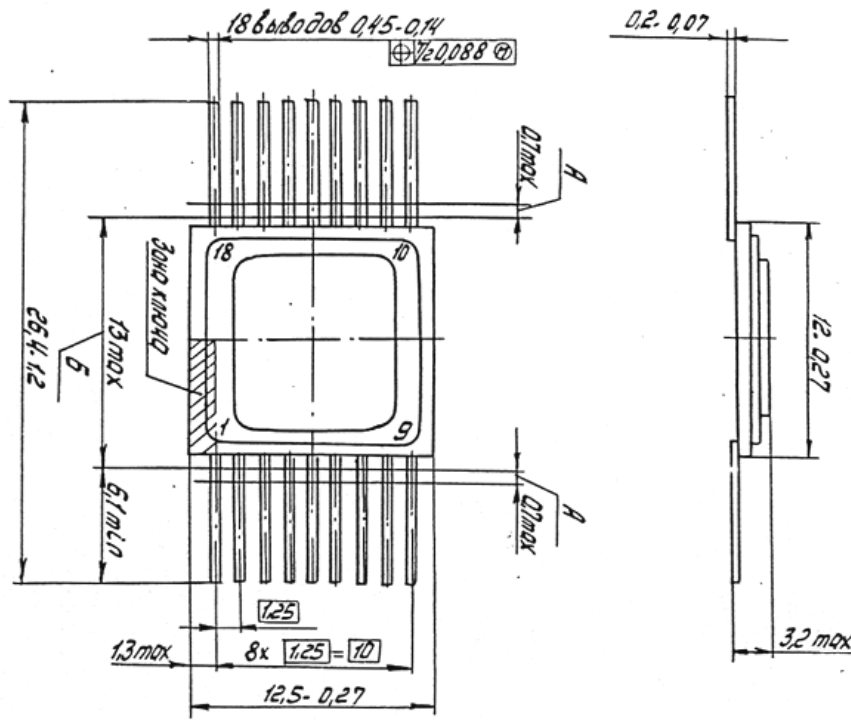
Габаритный чертеж корпуса 427.18-2.03
